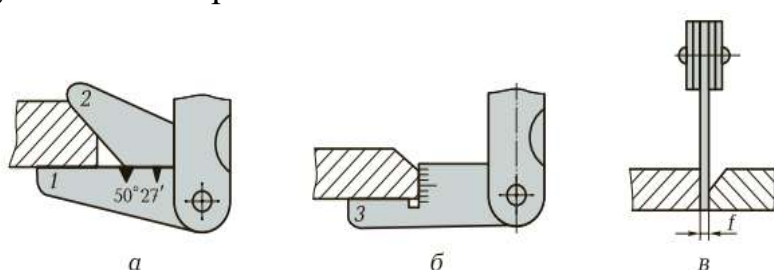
Применение шаблонов марки ШС-2: а — проверка угла разделки кромок; б — проверка притупления; в — проверка зазора; 1 ... 3 — номера пластин; f — зазор между кромками.
